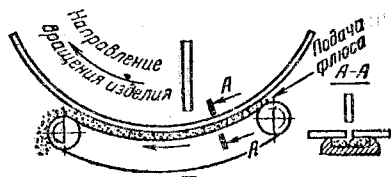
Стэнд для сварки кольцевых швов — а и флюсоремная подушка — б
